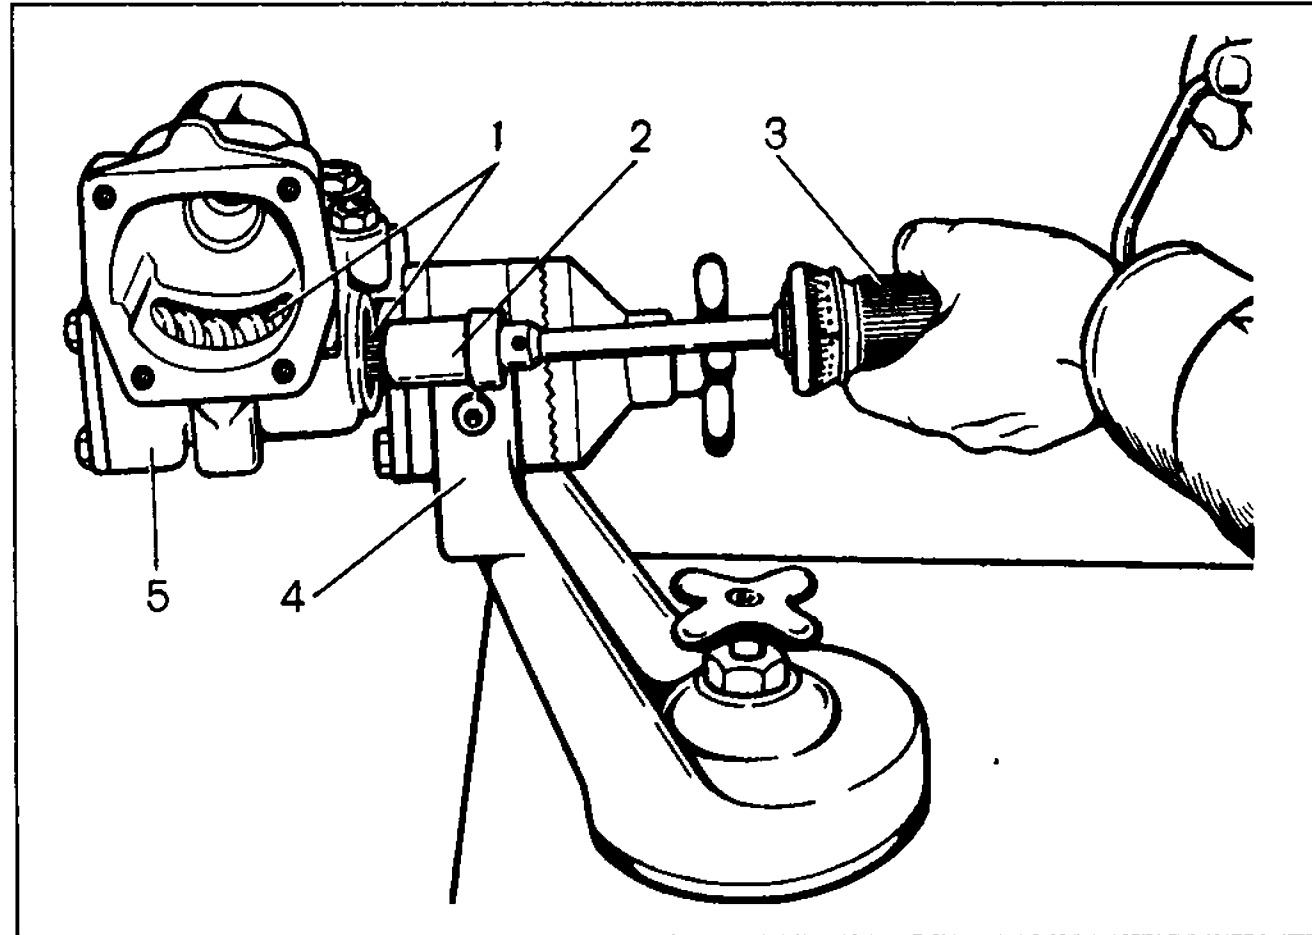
Контроль момента трения червяка динамометром: 1-червяк; 2-головка А.95697/5; 3-динамометр 02.7812.9501; 4-кронштейн стенда для ремонта редуктора рулевого механизма; 5-редуктор рулевого механизма
